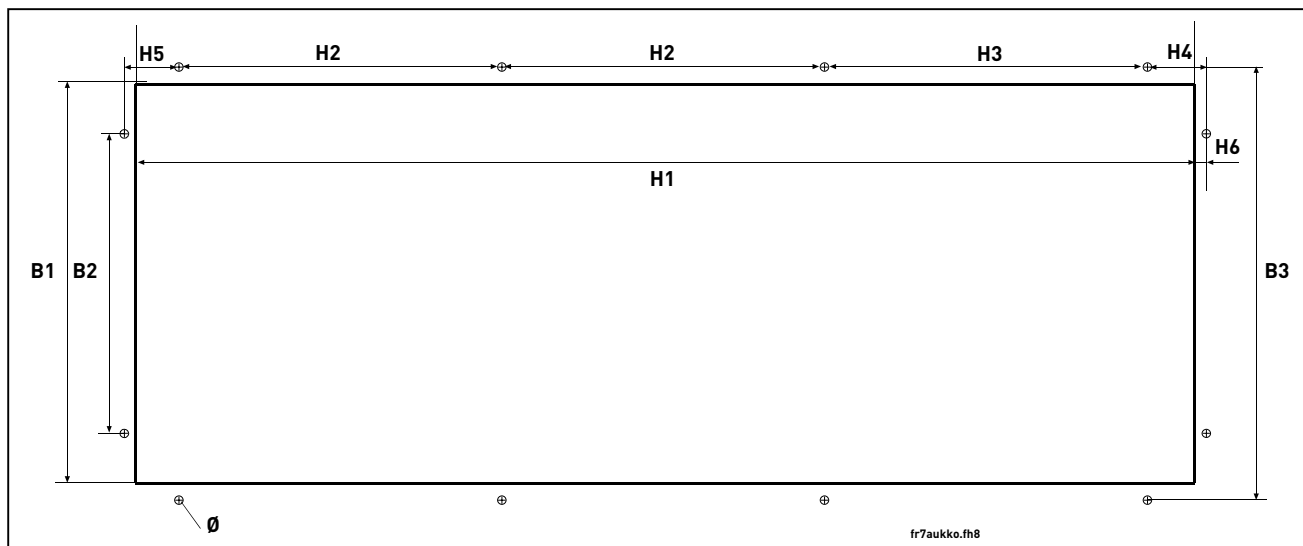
Vacon NX-dimensioner, IP21 med flange, FR7 og FR8
